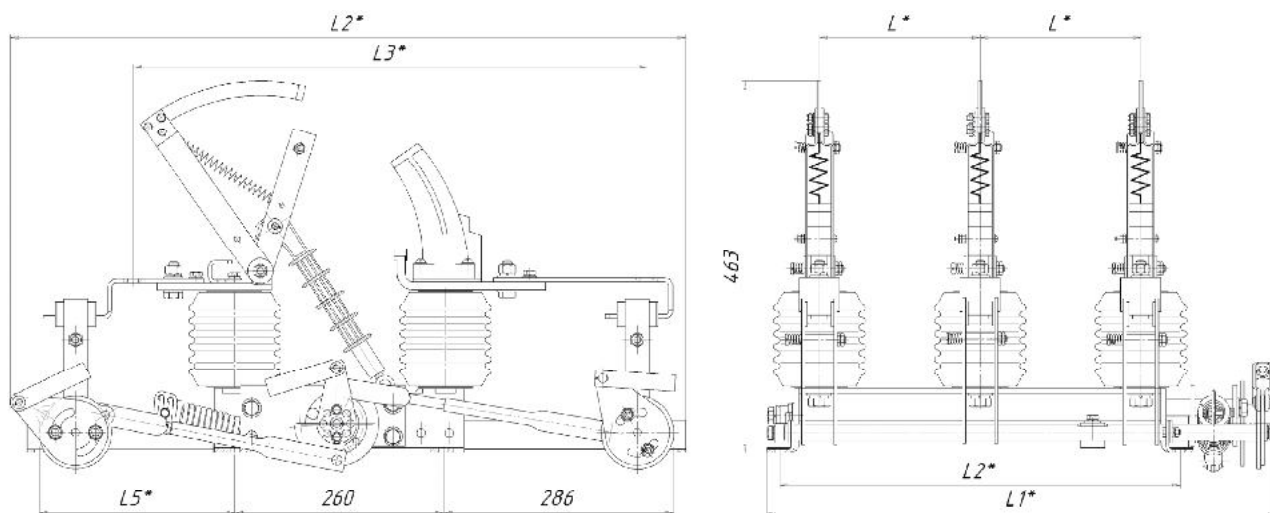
Выключатель нагрузки автогазовый с предохранителями ВНАП-10/630-20
